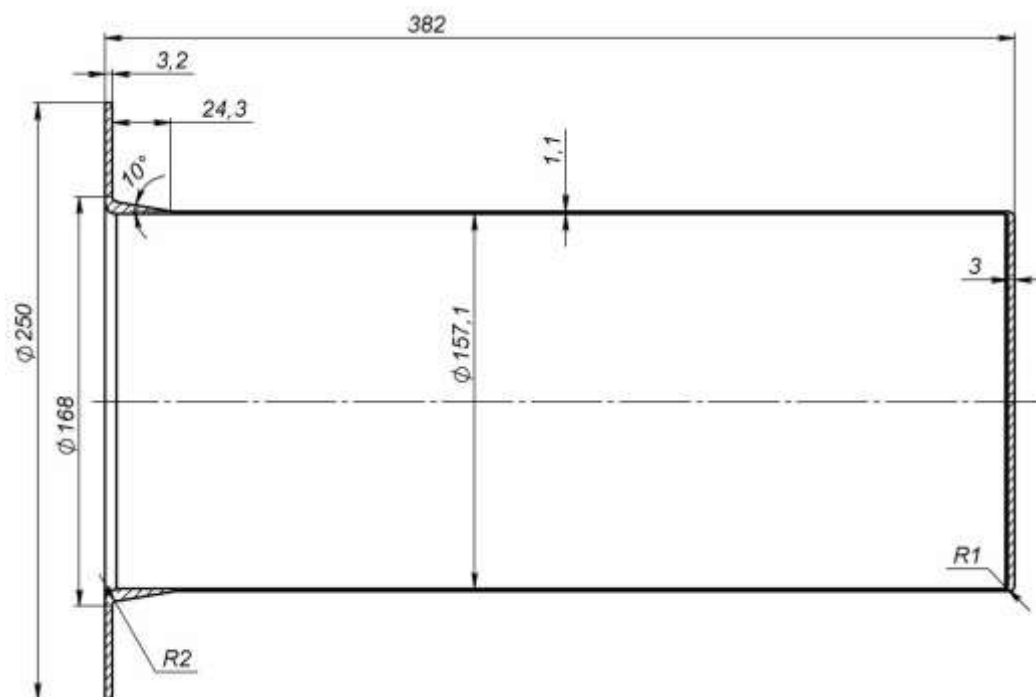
Эскиз детали кожуха, полученный многопереходной вытяжкой с утонением
